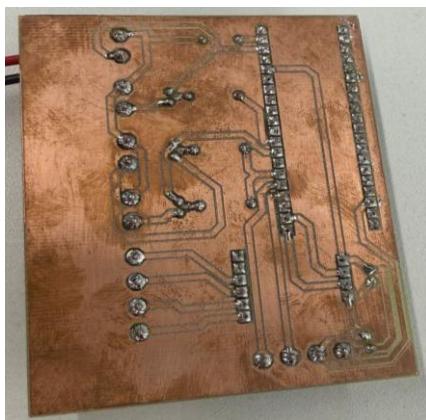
Trilhamento inferior da PCB, mostrando conexões e soldagem.
